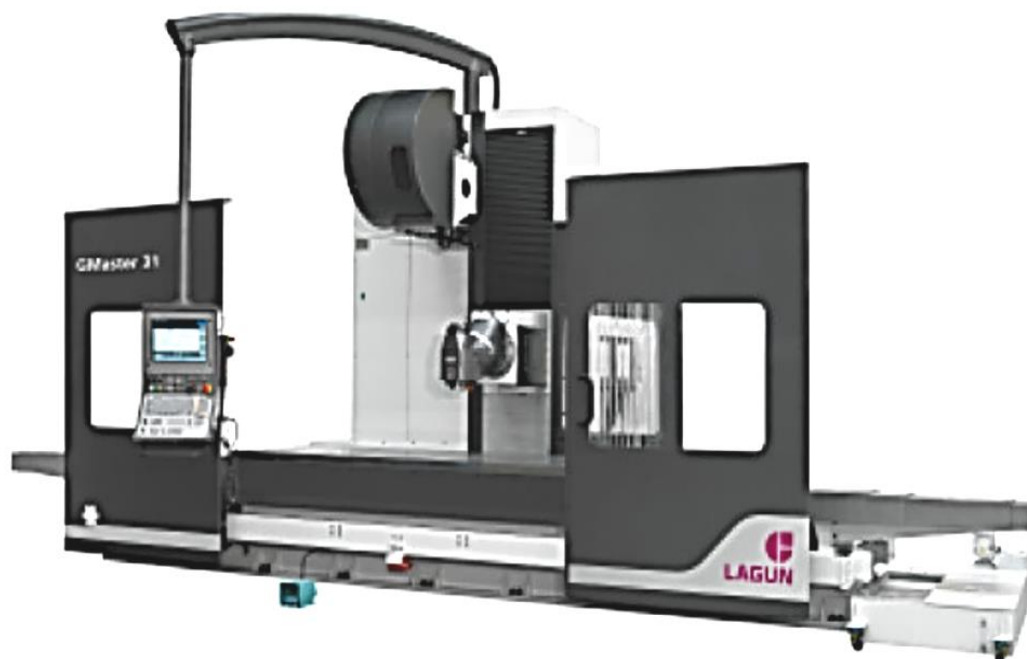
Стол фрезерный станок с поперечно-скользящей передней бабкой
